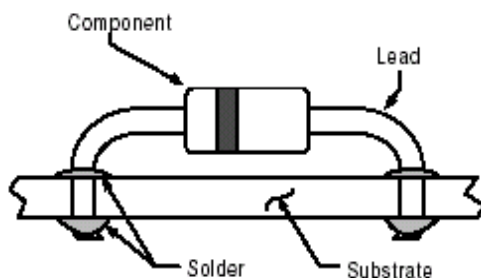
Esquema de unión de circuito con soldadura
